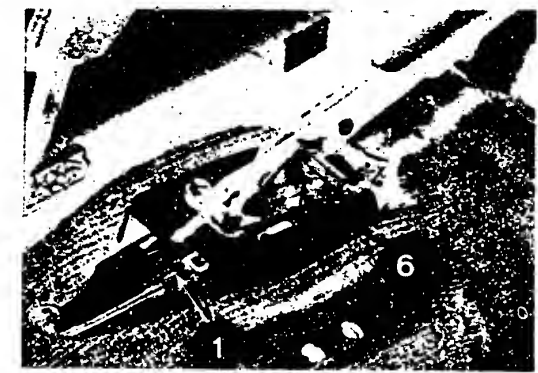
Handbremse mit der Einstellschraube für den Kabelzug.
